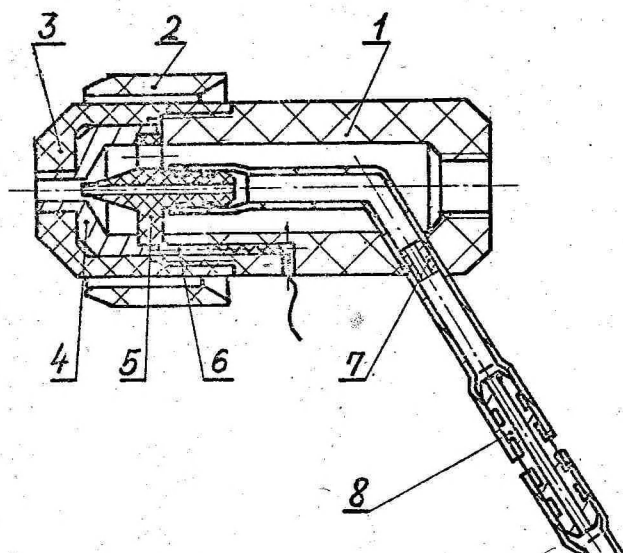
Усовершенствованный распылитель: I - корпус; 2 - кольцевая насадка; 3 - изолятор индуцирующего электрода; 4 - индуцирующий электрод; 5 - жидкостное сопло с фланцем; 6 - штифт; 7 - распорная втулка; 8 - соединительный штуцер; 9 - пружина; 10 - провод питания; II - трубка подачи жидкости.
